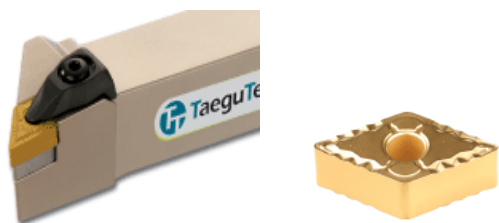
Сборный токарный резец со сменной многогранной пластиной TT8125
